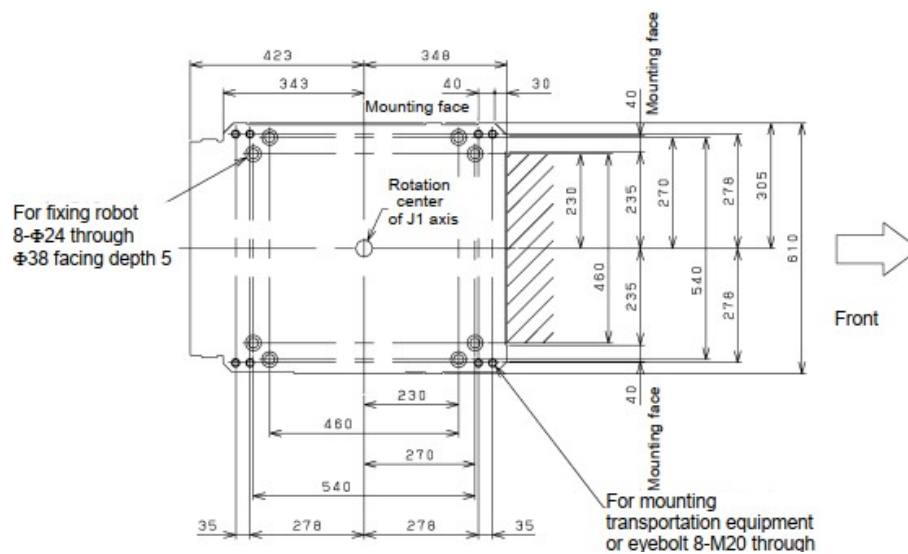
Dimensiones de la base del robot con puntos de anclaje.
